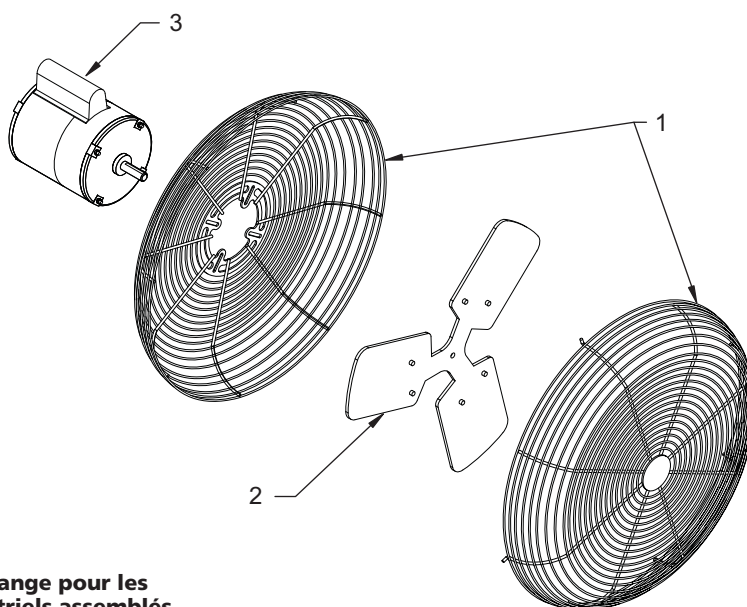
Pièces de rechange pour les ventilateurs jaunes industriels assemblés
